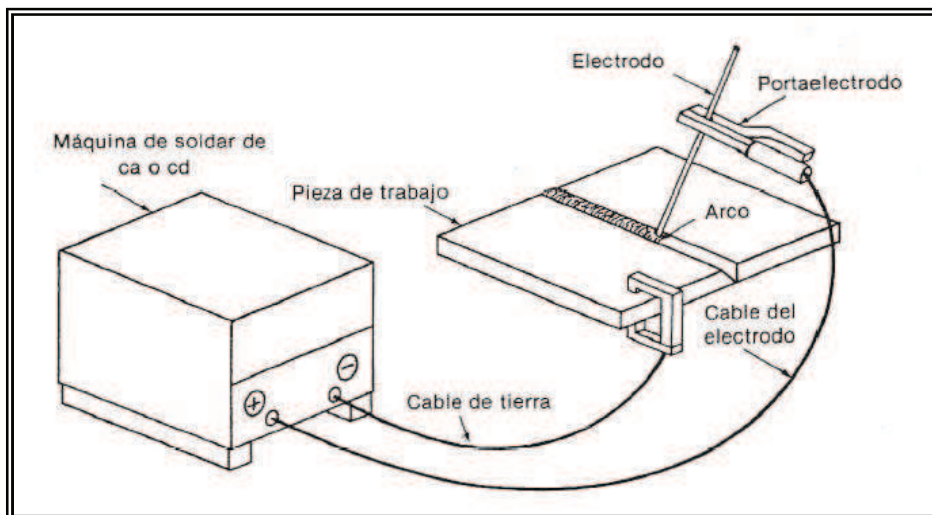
Disposición de elementos para soldadura de arco.
